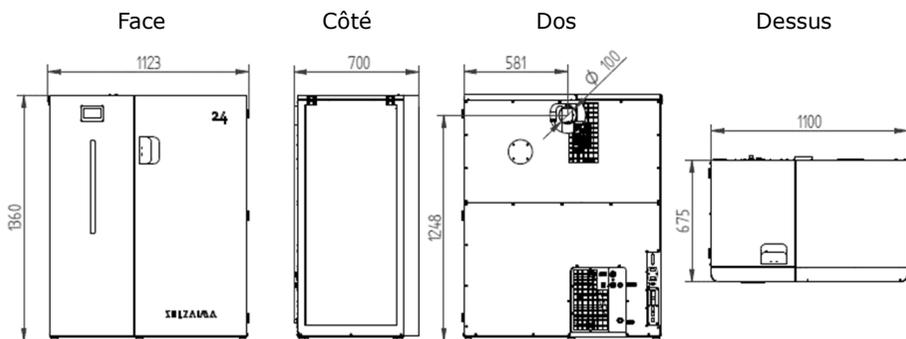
B - Dimensions de la chaudière SZM A PLUS 24 kW
